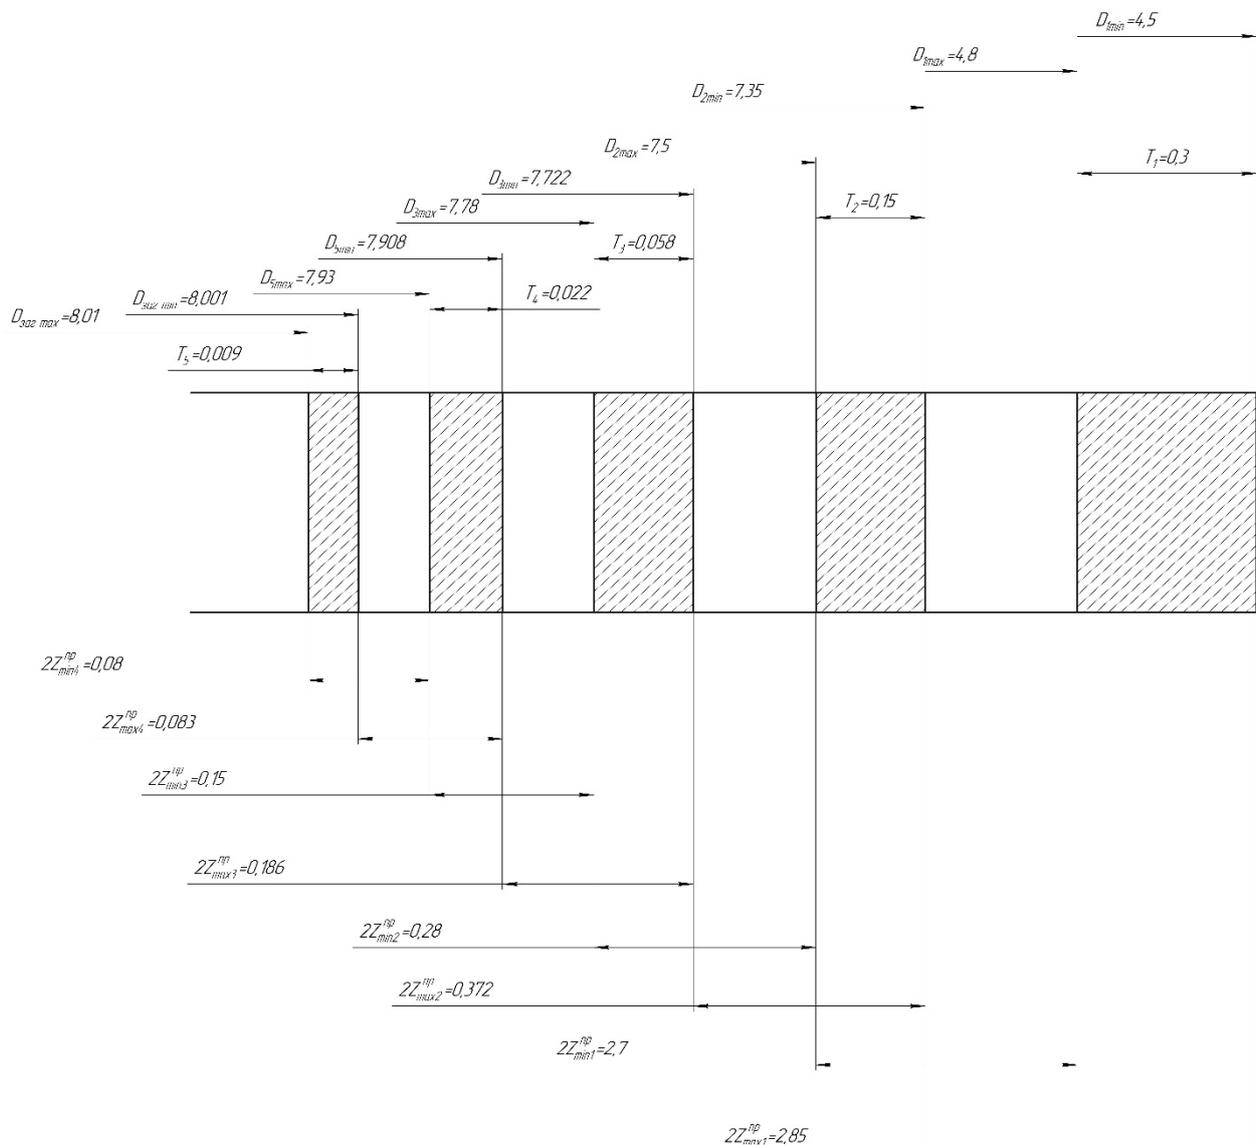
Схема расположения припусков, допусков и размеров
